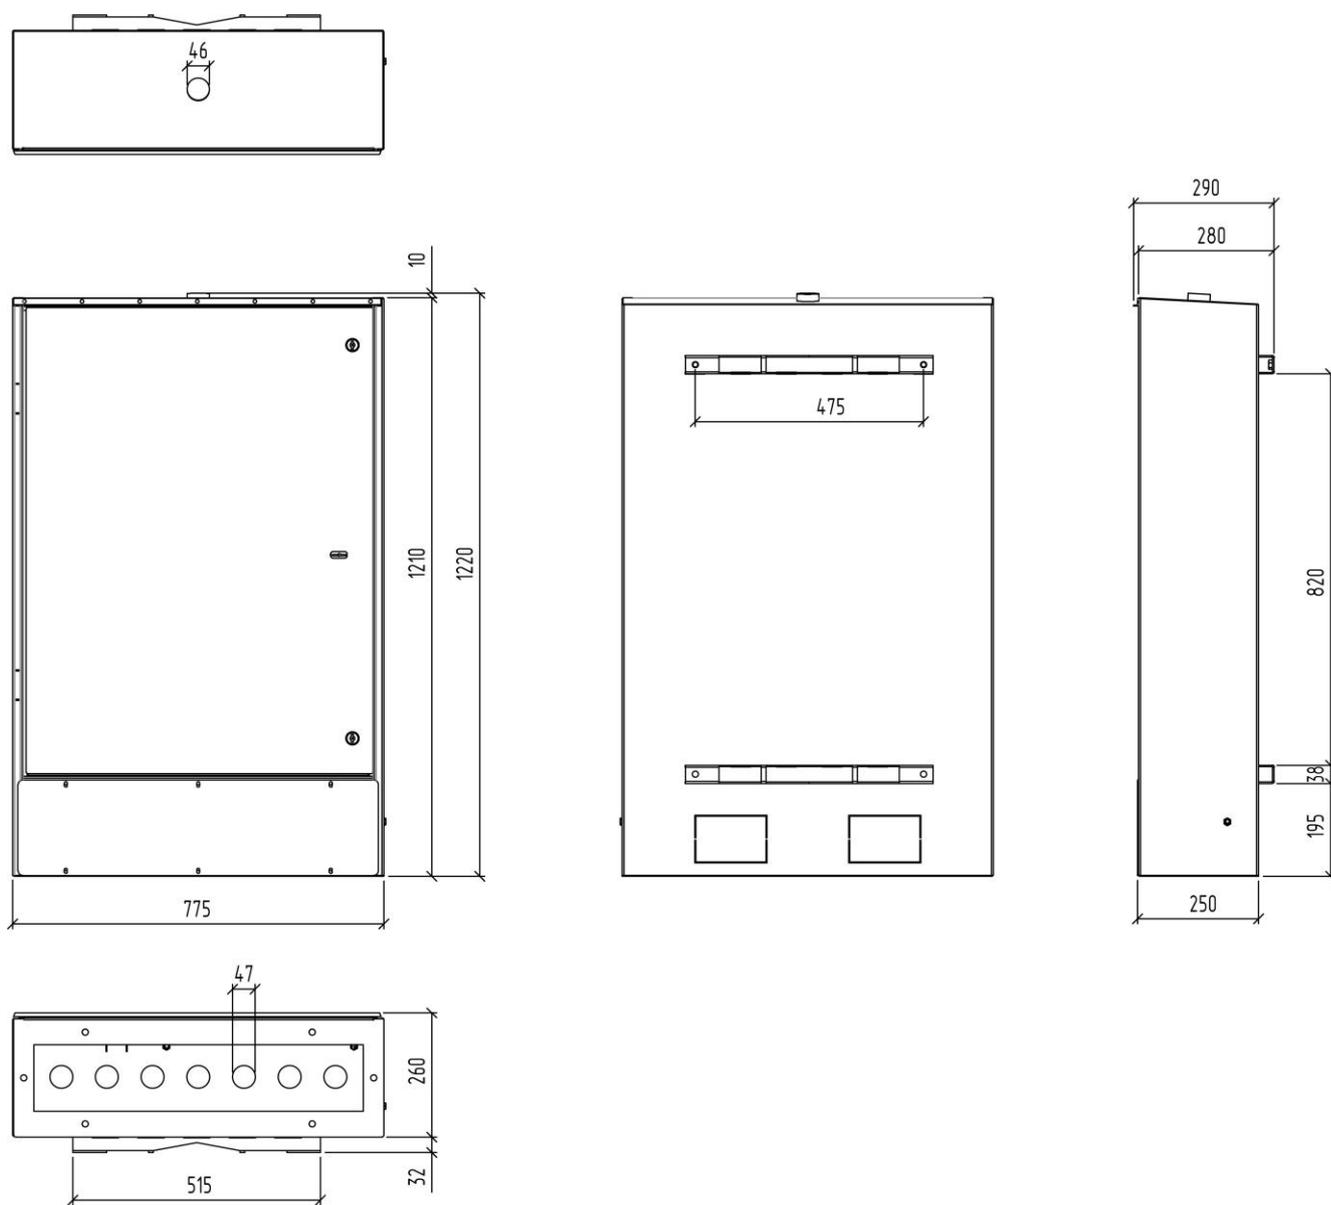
Габаритные и установочные размеры АПВ (конструктив К2)
